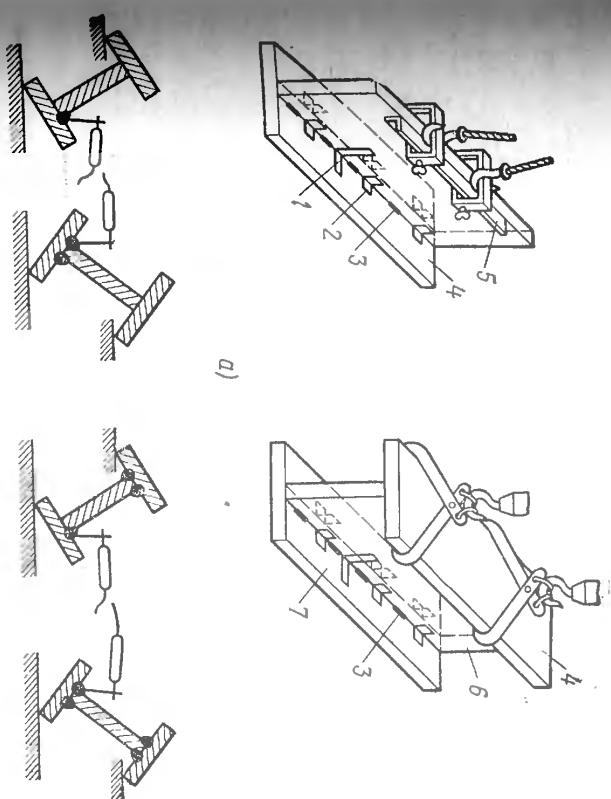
Схема сборки балок по разметке (а) и последовательность наложения швов (б):
